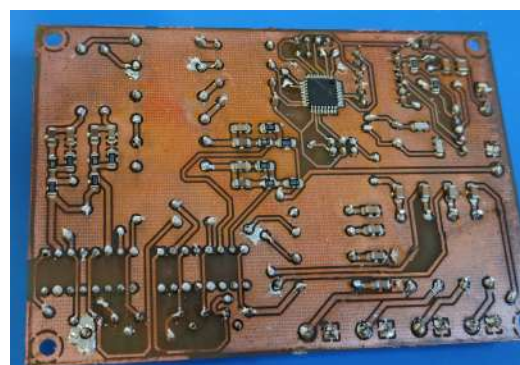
Imagen del reverso de la *PCB* tras ser soldados sus componentes
